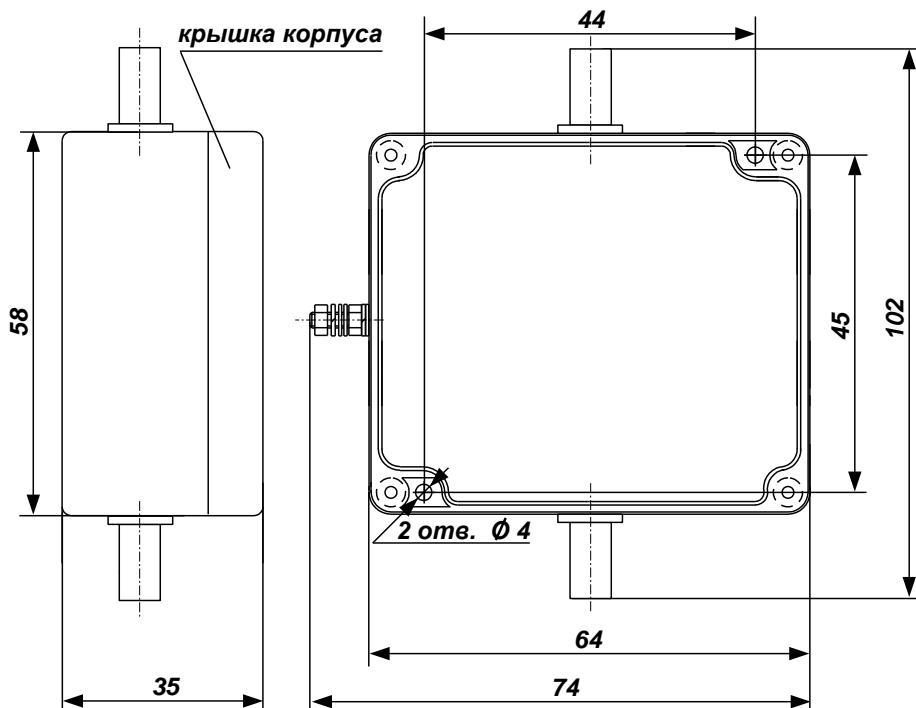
Габаритные и присоединительные размеры БЗВВ-01К
